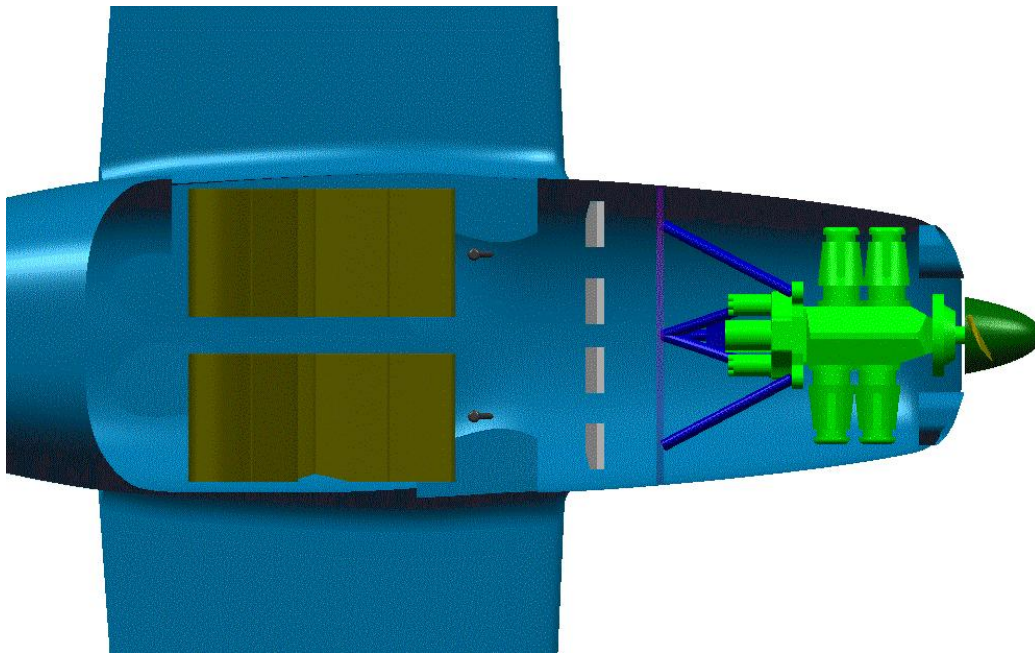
Dimensões da Cabine e Instalação do Motor – Vista de Planta
